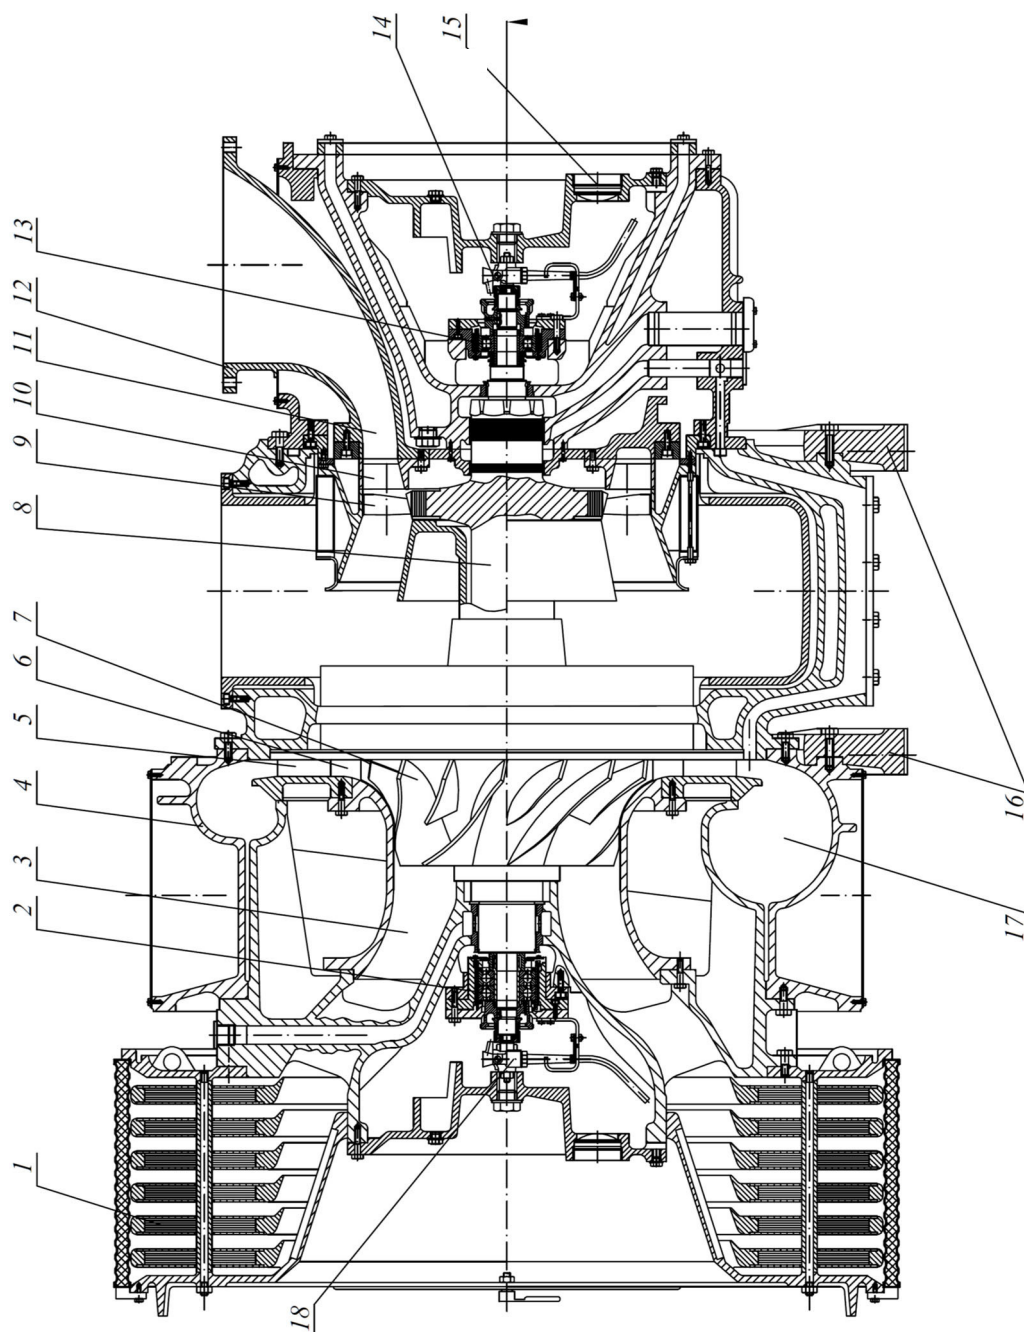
Турбокомпресор типу VTR714D: 1 – фільтр-глушник; 2 – підшипниковий вузол; 3 – повітряна камера; 4 – корпус компресора; 5 – лопатковий дифузор; 6 - безлопатковий дифузор; 7 – робоче колесо компресора; 8 – ротор; 9 - робоче колесо турбіни; 10 – направляючий апарат; 11 – камера підвода газу; 12 – газоприйомний патрубок; 13 - підшипниковий вузол; 14 – масляний насос; 15 – оглядове скло; 16 – лапи; 17 – завитка; 18 - масляний насос
